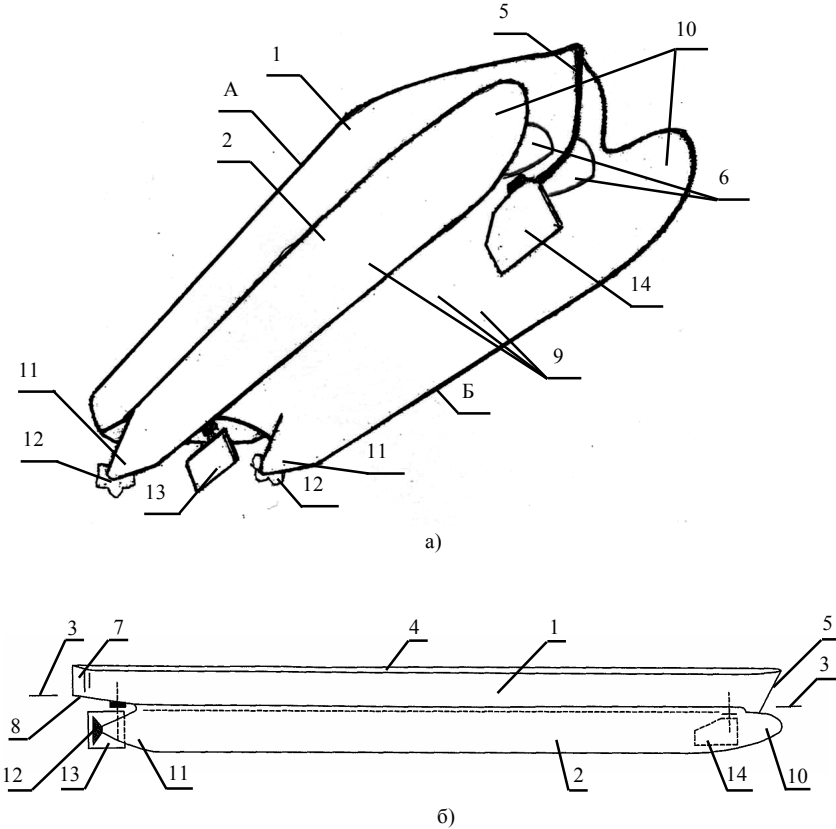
Вид корпуса судна: а) вид корпуса судна в изометрической проекции; б) фронтальный вид судна:
